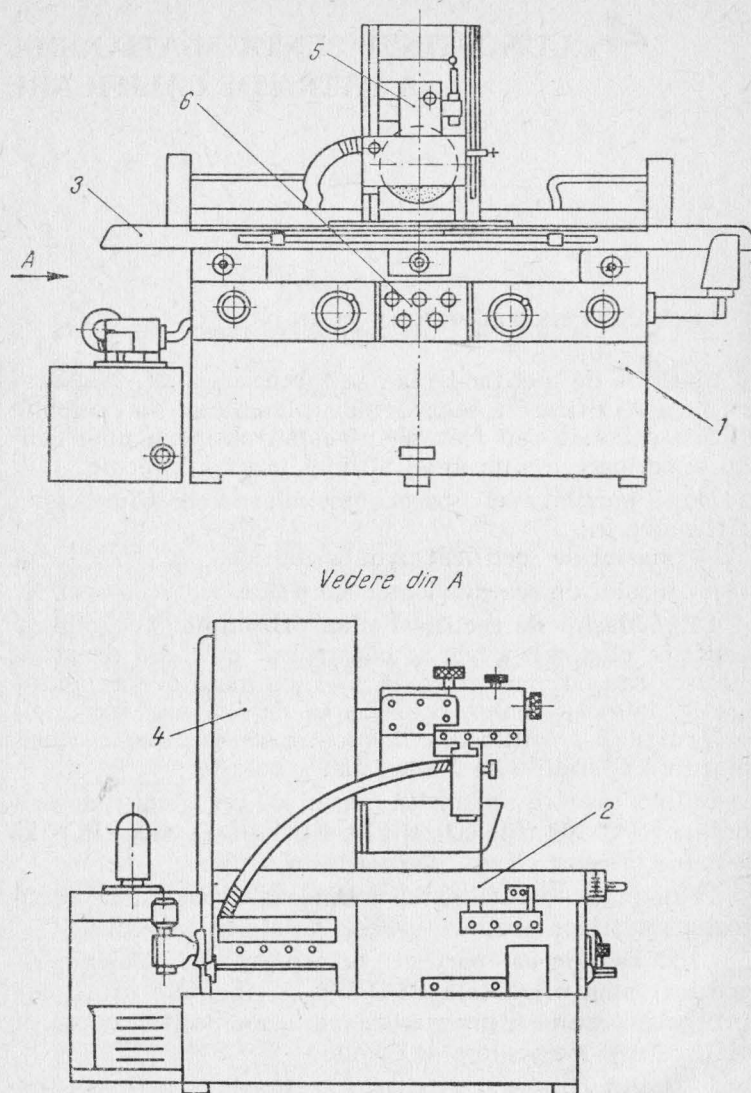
Mașina de rectificat plan orizontal RPO 200.
